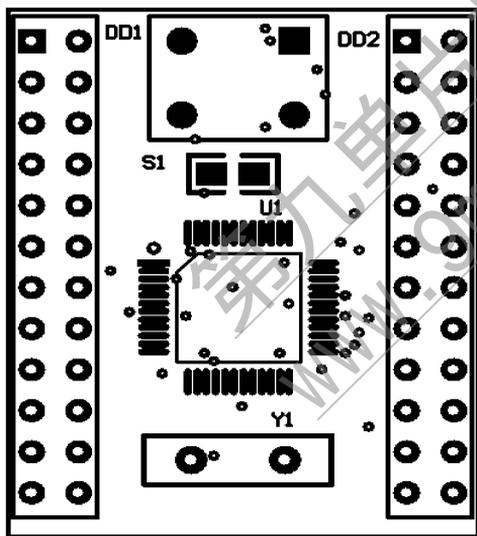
LM3S615 微控制器 PACK 板电路和 PCB 图
